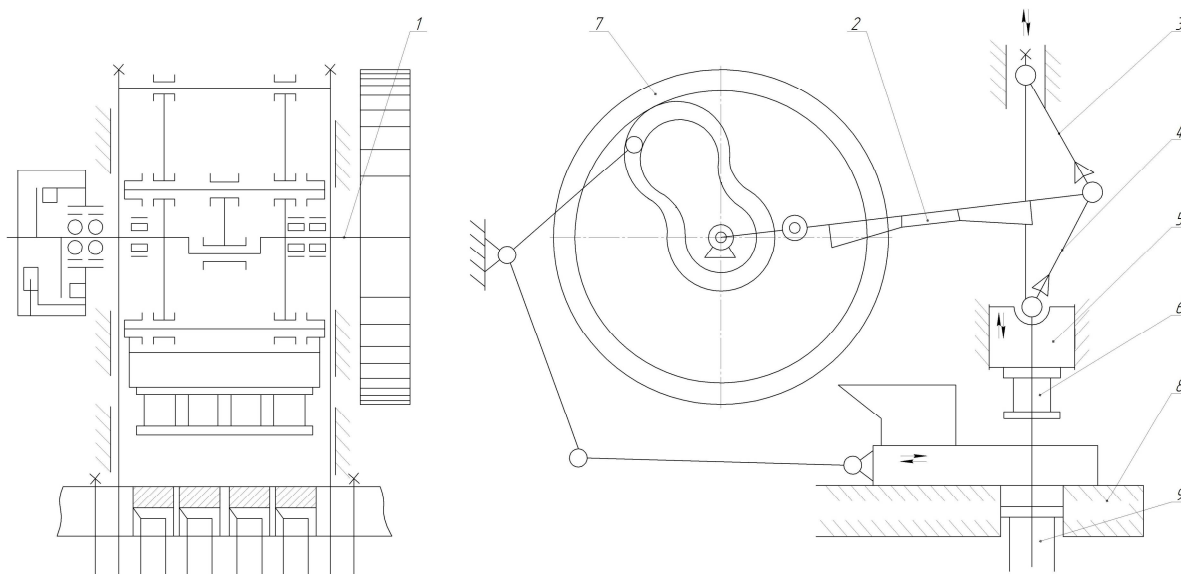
Кінематична схема вузла пресування пресу СМ-1085А:
